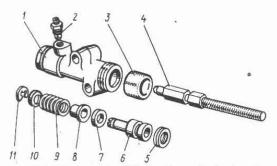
Piezas del cilindro de mando de desembrague (del cilindro de trabajo): 1 - cuerpo; 2 - racor; 3 - casquete; 4 - empujador; 5 - anillo de empaquetadura; 6 - émbolo; 7 - anillo de empaquetadura; 8 - platillo; 9 - muelle; 10 arandela; 11 - anillo de fijación
